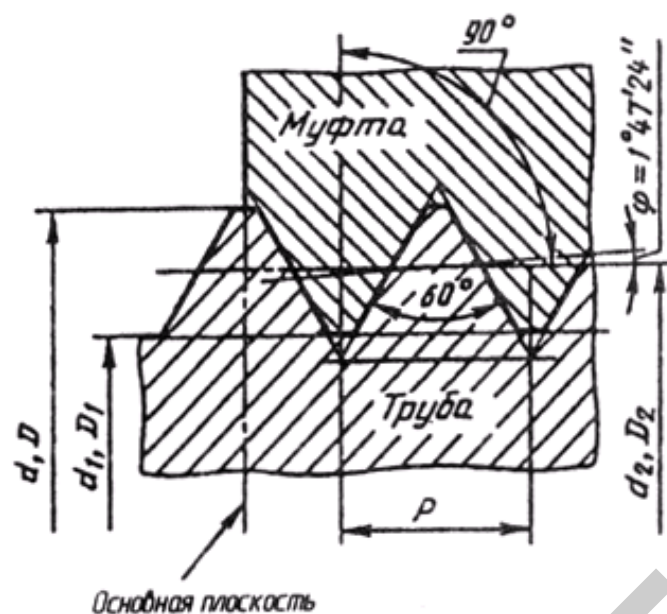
Профиль и основные параметры конической дюймовой резьбы
